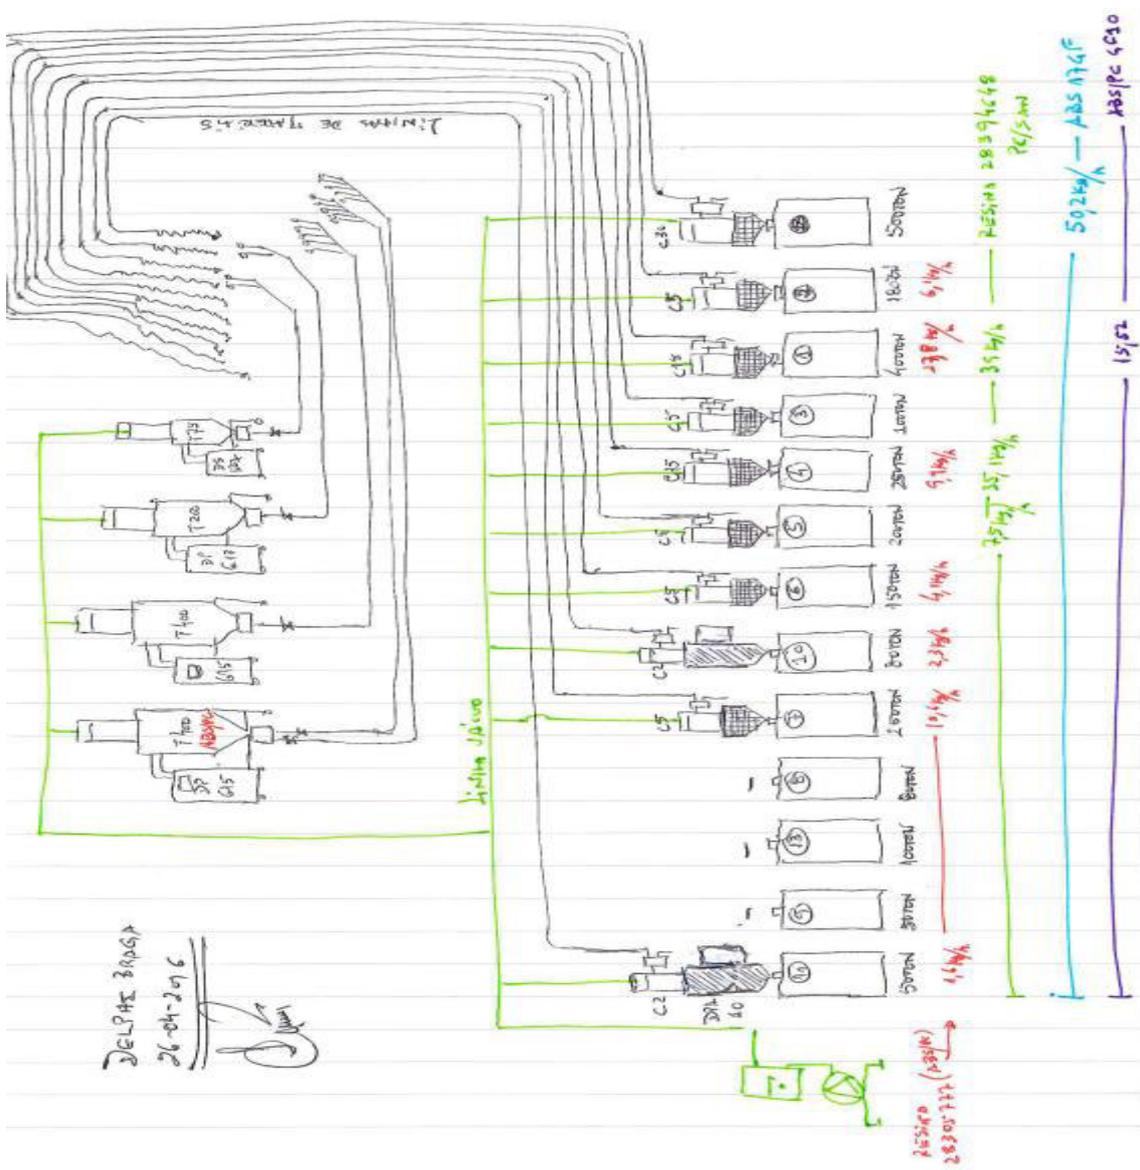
Layout da proposta 1 (PINHEIRO, 2016)
